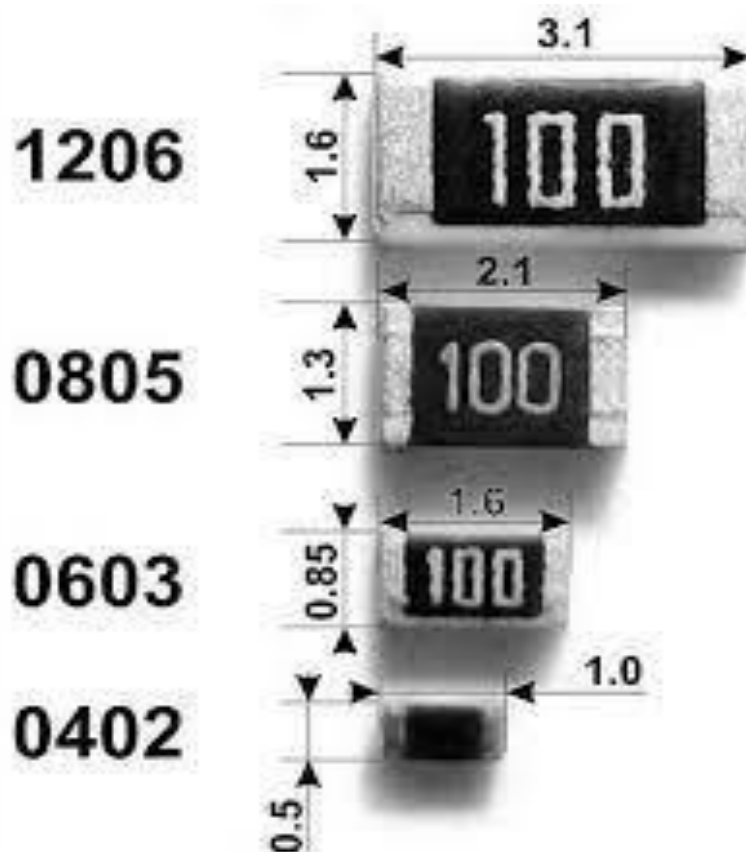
Стандартні розміри SMD компонентів.
